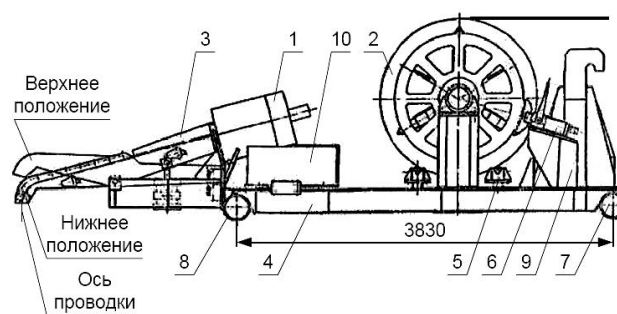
Схема установки для ввода стальной ленты в кристаллизатор на металлургическом предприятии «Азовсталь» [1, с. 116]: 1 – тянуще-правильное устройство; 2 – кассета; 3 – направляющая; 4 – рама; 5 – опорные катки; 6 – устройство для торможения; 7, 8 – колеса установки; 9 – маршевый двигатель; 10 – двигатель тянуще-правильного устройства
